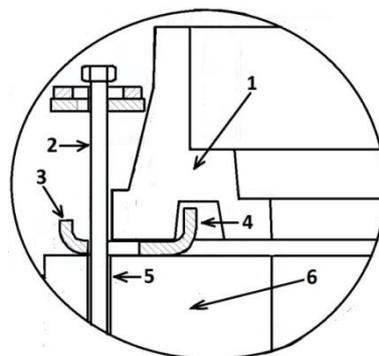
Положение швеллера в выемке корпуса люка ППЛ:
